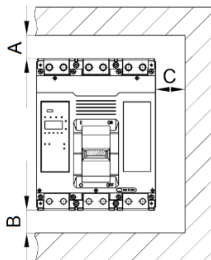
Габаритные и установочные размеры выключателей PRO.KVANT S1 типоразмера 1600
